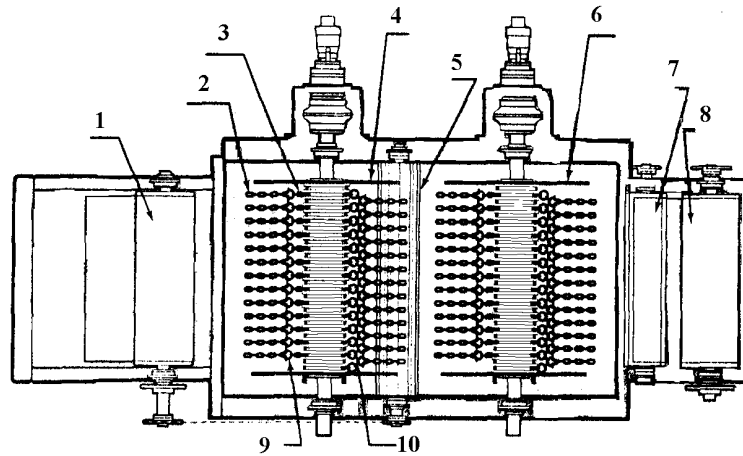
Горизонтальный цеповой окорочный станок фирмы Manitowoc HFDD-1858 Delimber / Debarker (вид сверху) [108]
